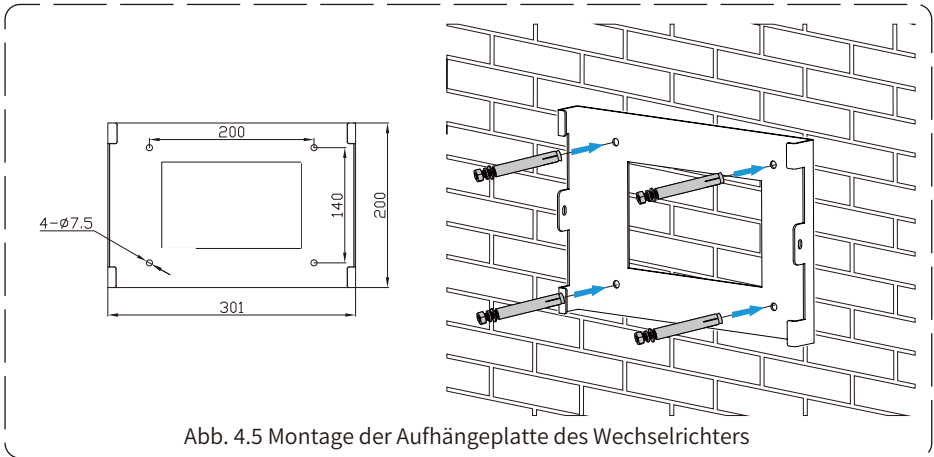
Montage der Aufhängeplatte des Wechselrichters
